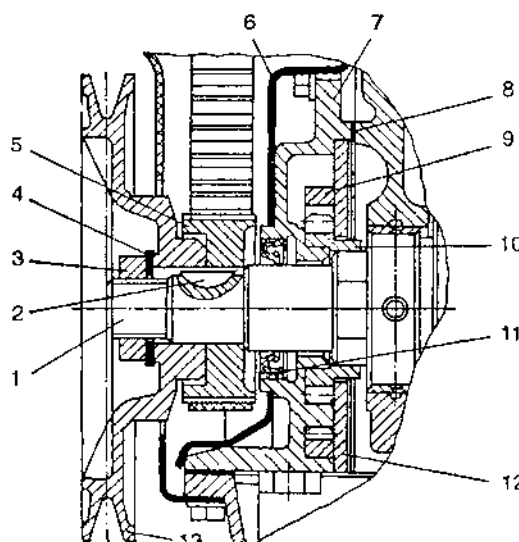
Носок коленчатого вала со шкивом:
